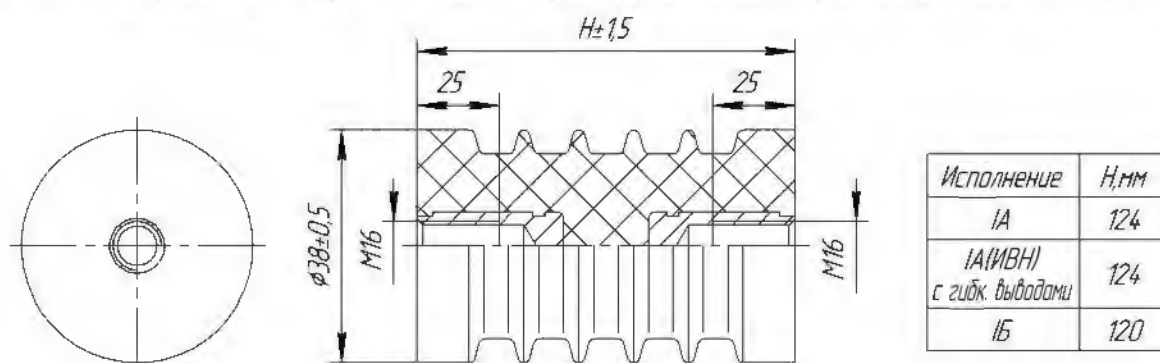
Габаритные и установочные размеры изолятора опорного ИОЛ-4/10 II.
